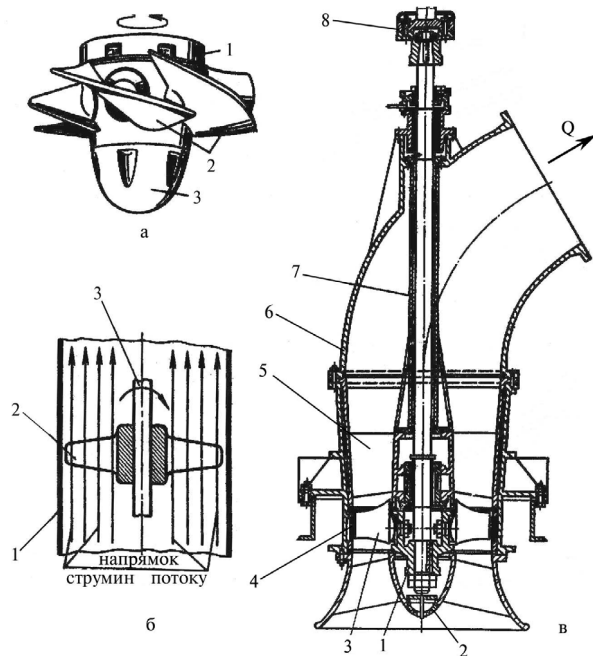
Схема вісьового насоса: а – робоче колесо; б – рух потоку рідини в насосі; в – насос; 1 – втулка; 2 – передній обтікач; 3 – лопаті; 4 – робоча камера; 5 – виправляючий апарат; 6 – корпус насоса; 7 – вал; 8 – муфта з’єднання з електродвигуном.
